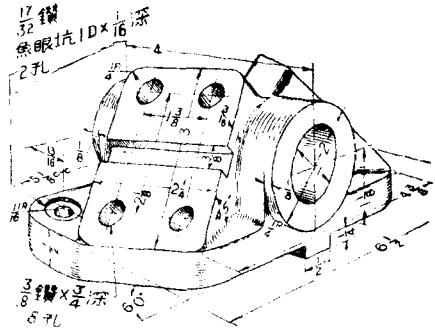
斜面工具底座 (Chamfer Tool Base).
